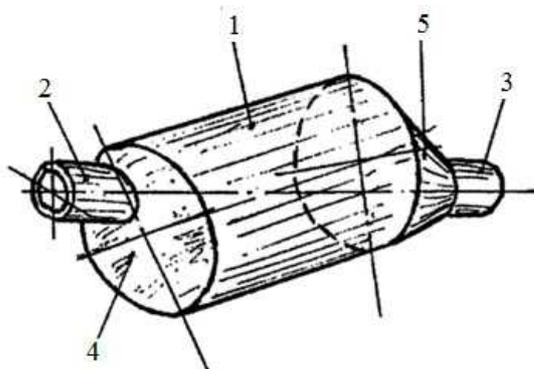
Рабочий орган в виде барабана устройства для приготовления кормов: 1 – барабан; 2, 3 – загрузочная и разгрузочная цапфы;
